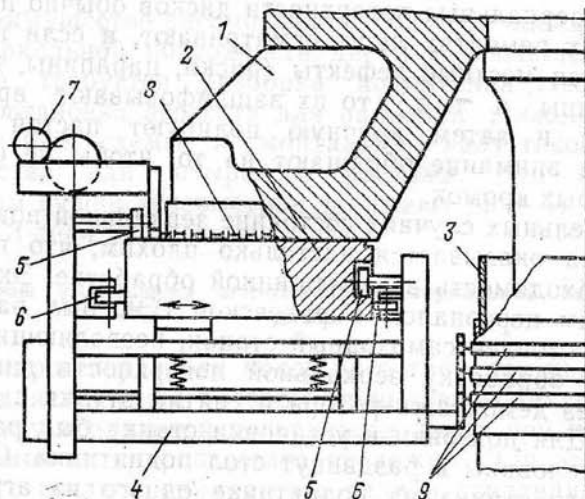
Установка станка в подпятнике для обработки поверхности диска.
